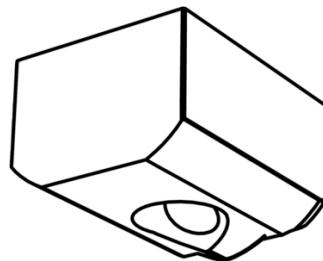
Сварочный башмак для сварки шва переменного сечения
